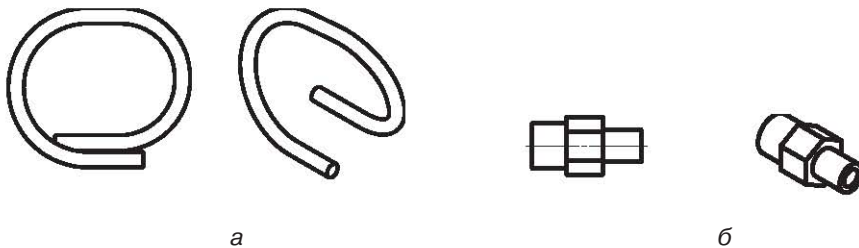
Изображения деталей сборки кабеля: а — кабель; б — вилка (розетка)
